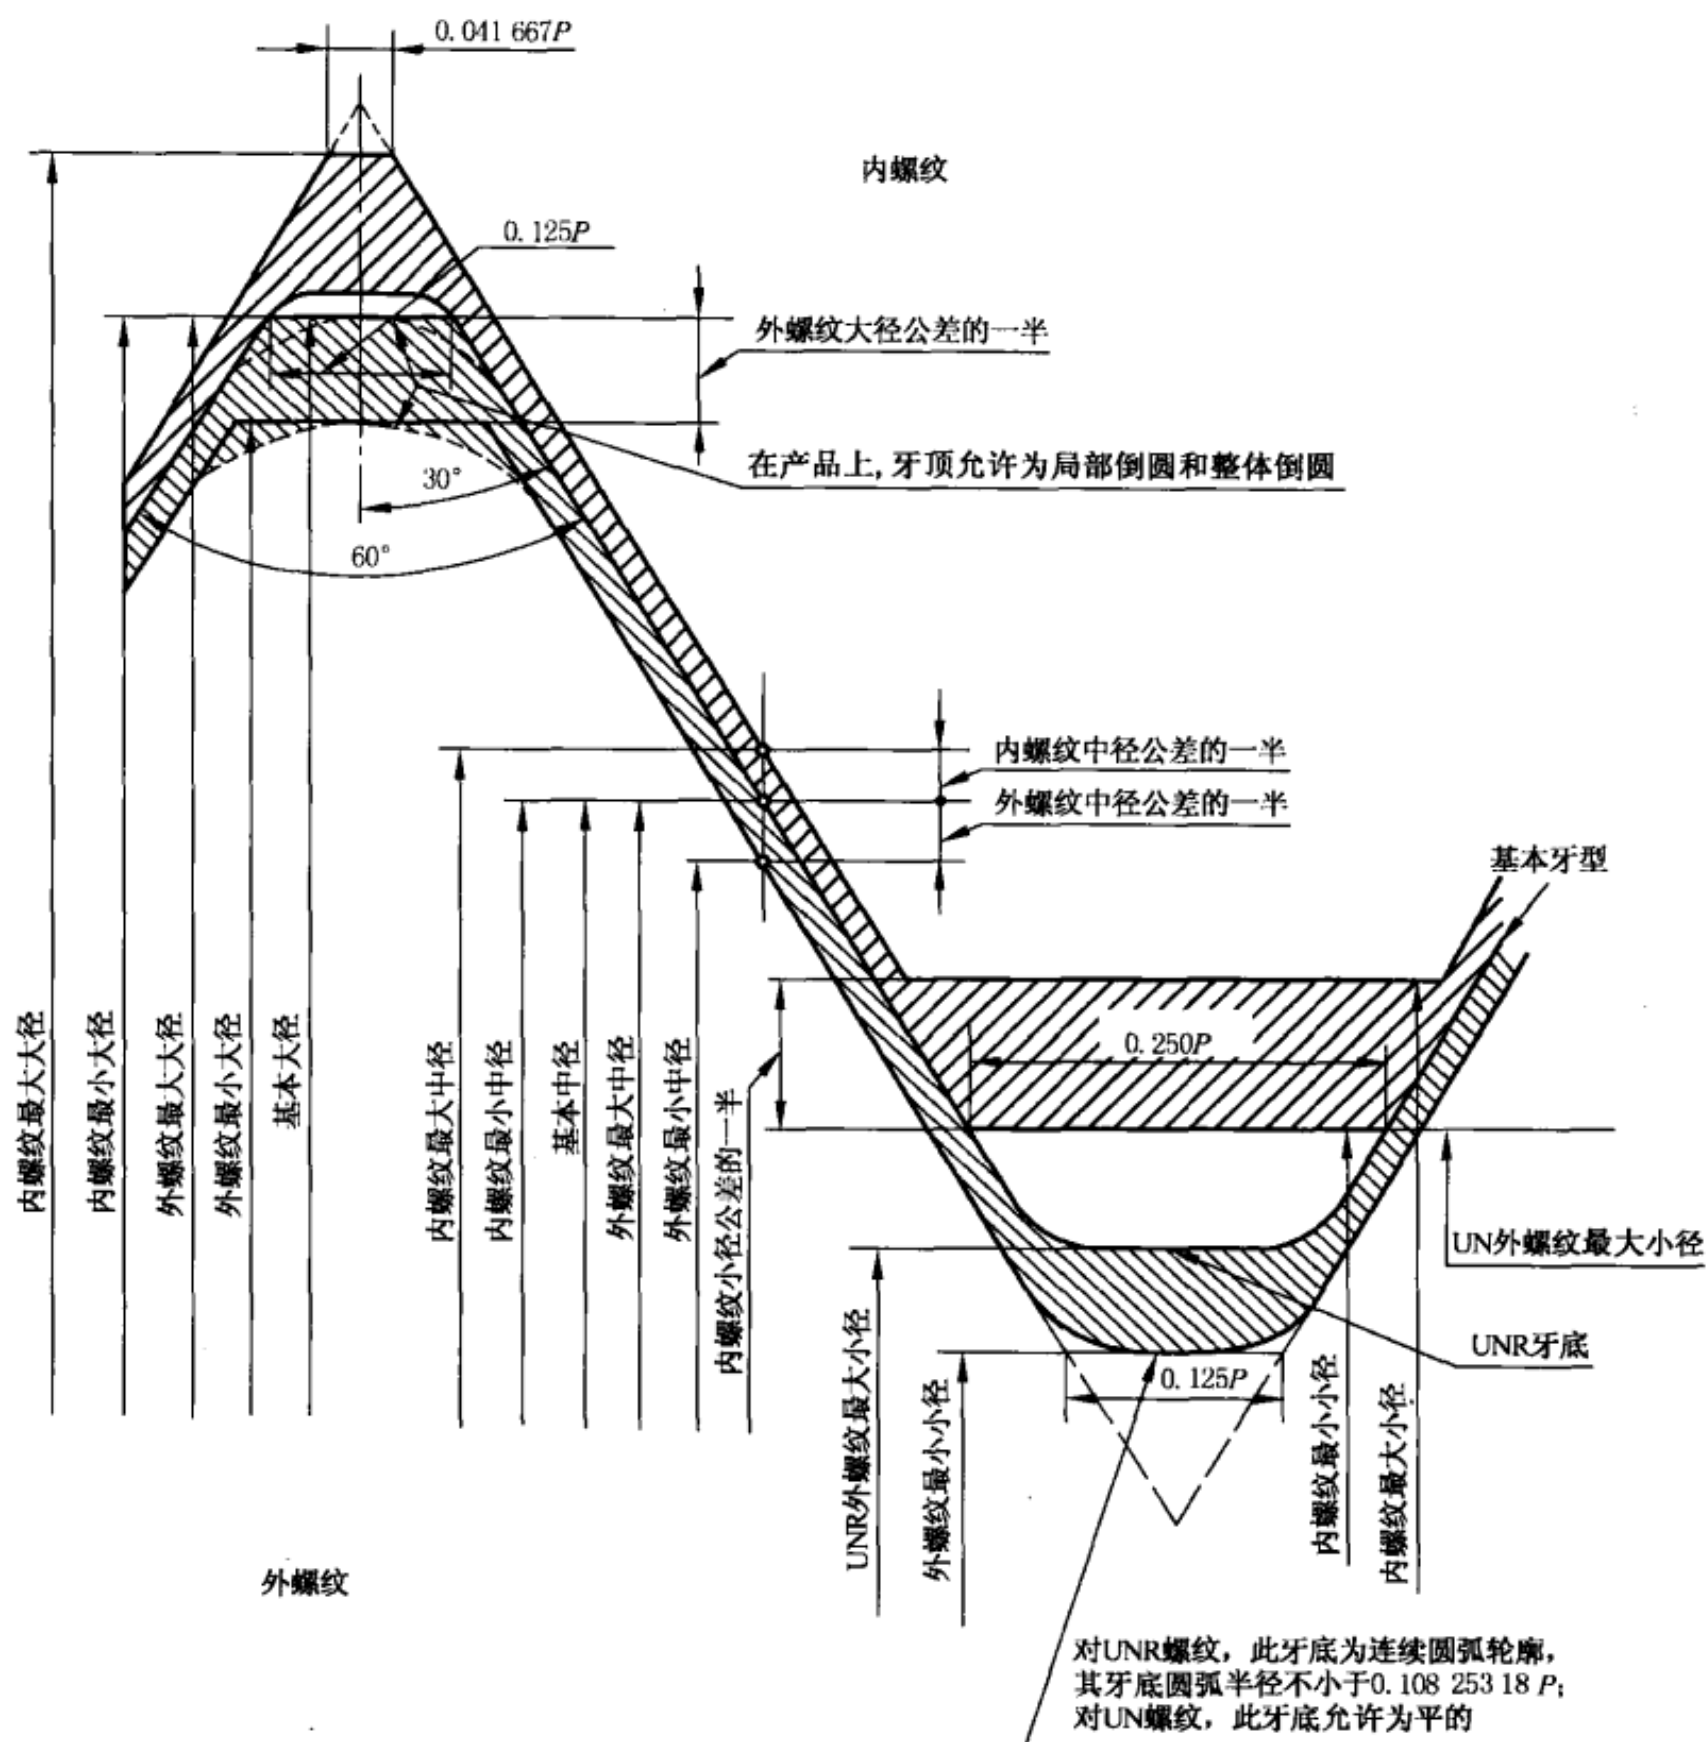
3A 和 3B 统一螺纹的公差带位置
